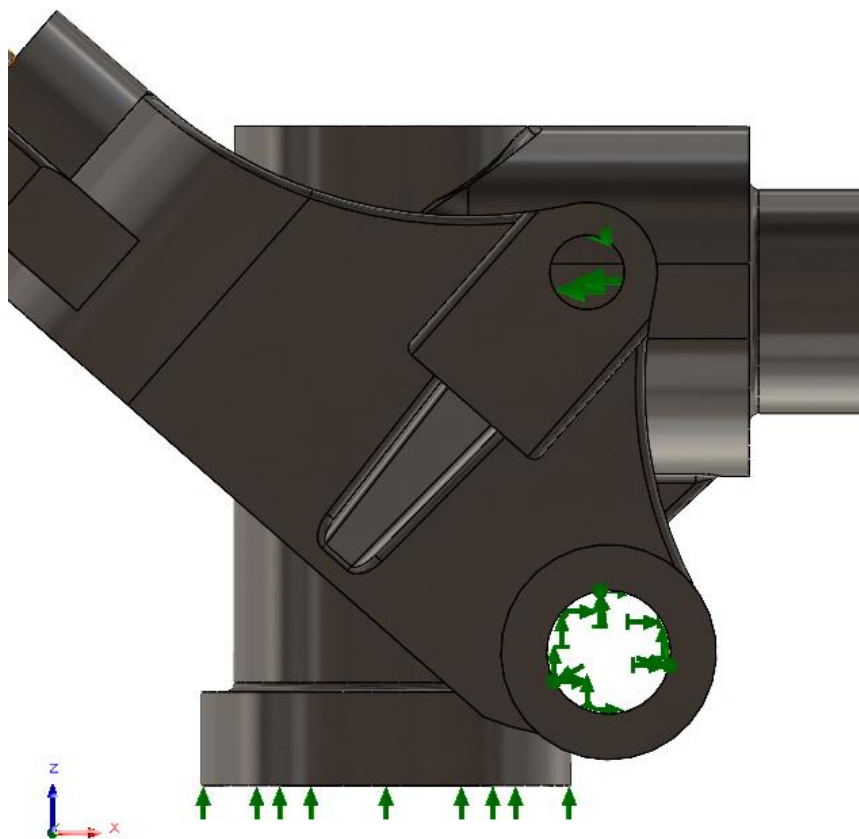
Constrangimentos aplicados no 1º Estudo.
